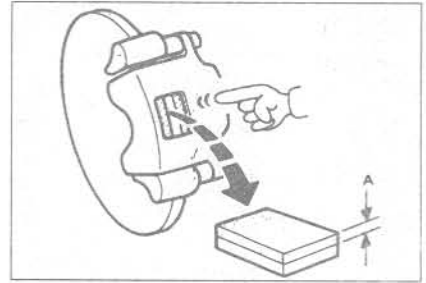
Проверка остаточной толщины материала трения тормозной колодки (Глава 12)
